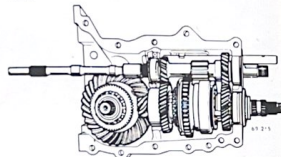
Semicaja izquierda alojando todo el conjunto de engranajes y diferencial.
